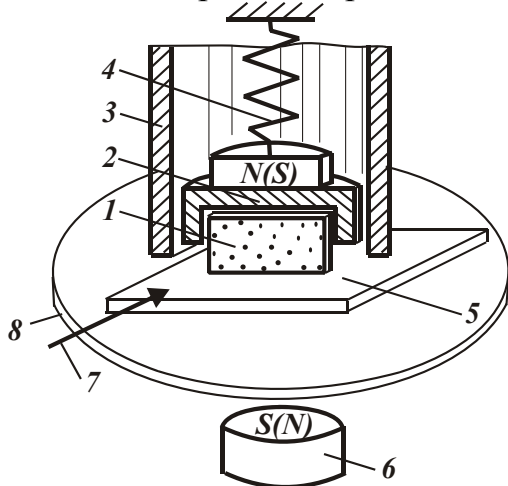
Схема магнито-импульсного шлифования с применением вращающегося стола: 1 – шлифовальный круг; 2 – патрон для шлифовального круга с электромагнитом; 3 – направляющий цилиндр, по которому перемещается патрон с шлифовальным кругом; 4 – пружина подвески патрона с шлифовальным кругом; 5 – обрабатываемая деталь; 6 – электромагнит; 7 – лазерный луч контроля размеров обрабатываемой детали; 8 – вращающийся стол.
